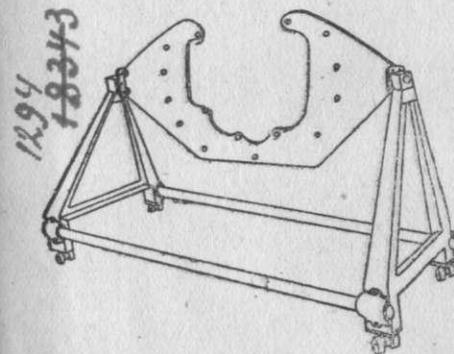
Поворотный станок типа Райт для сборки звездообразных моторов.
